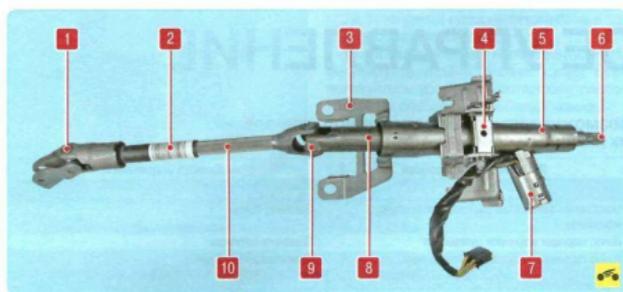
Рулевая колонка: 1 – нижний карданный шарнир промежуточного вала; 2 – наружная часть промежуточного вала; 3 – нижний кронштейн крепления рулевой колонки; 4 – механизм регулировки положения рулевой колонки; 5 – рулевая колонка; 6 – шлицевой наконечник рулевого вала; 7 – выключатель (замок) зажигания; 8 – рулевой вал; 9 – верхний карданный шарнир промежуточного вала; 10 – внутренняя часть промежуточного вала
